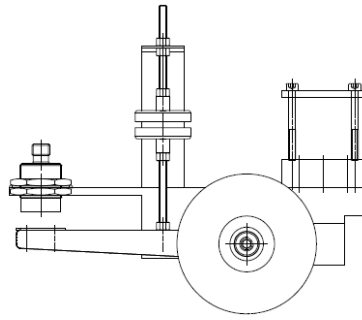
Mecanismo de deteção de emendas instalado noutras máquinas do grupo.
